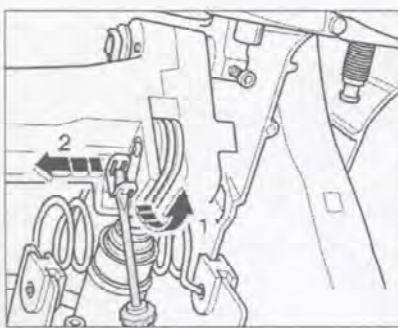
Приподнимите отверткой фиксатор (стрелка 1), извлеките штифт (стрелка 2) и отсоедините педаль от главного цилиндра сцепления.
